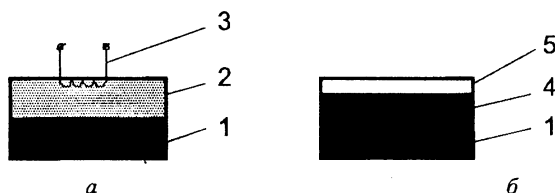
Схема СВС-наплавки: а) образец до наплавки: 1 — подложка с высокоэкзотермической шихтой 2; 3 — электроспираль; б) образец после наплавки: 4 — литое защитное покрытие; 5 — шлаковый слой
